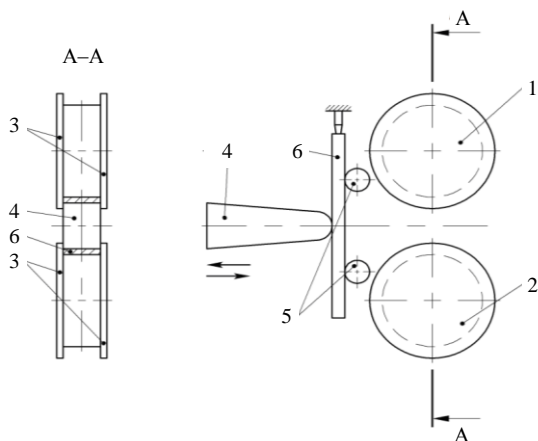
Схема прокатки профиля на оправке: 1, 2 – валки; 3 – реборды; 4 – оправка; 5 – ролики; 6 – прокатываемая полоса
